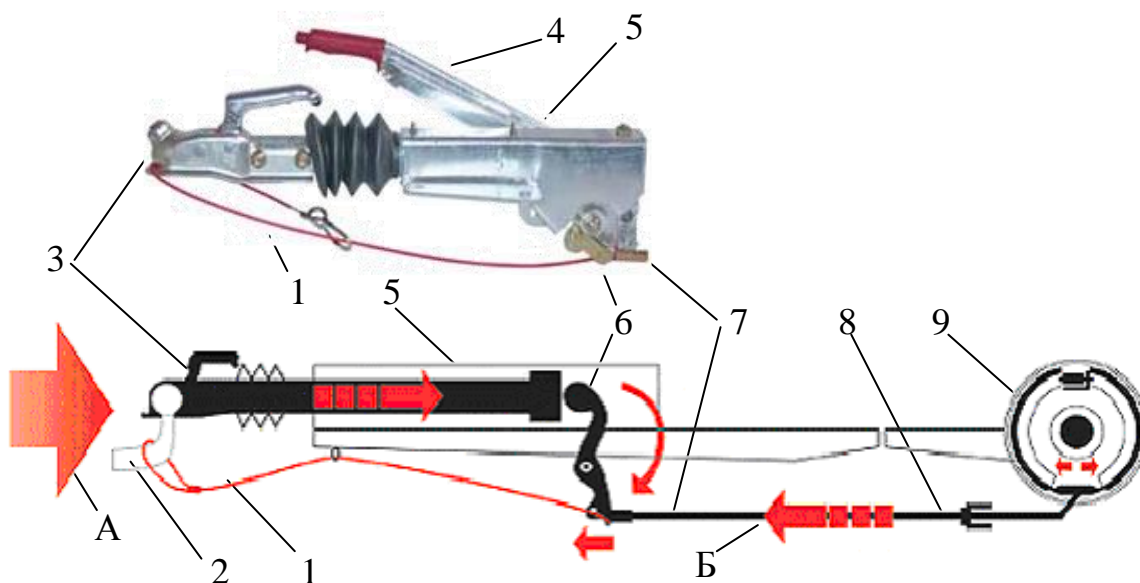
Схема механического привода инерционной тормозной системы прицепа легкового автомобиля 1 – трос привода аварийного торможения; 2 – фаркоп автомобиля-тягача; 3 – сцепное устройство прицепа; 4 – рычаг стояночного тормоза; 5 – дышло прицепа; 6 – передаточный рычаг; 7 – тяга; 8 – трос; 9 – тормозной механизм; А – направление реактивной силы от тягача при его торможении; Б – направление приводной силы
